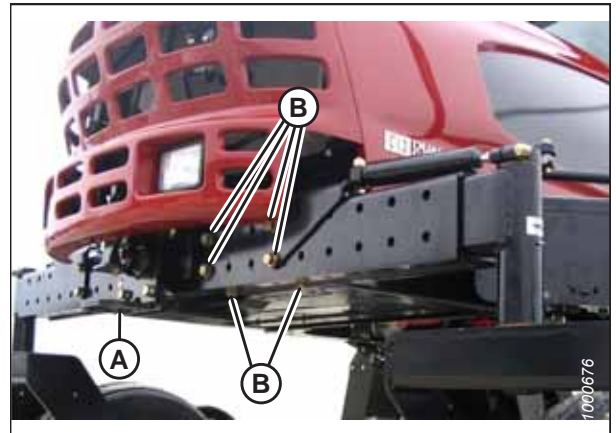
Удлинитель самоустанавливающегося колес
